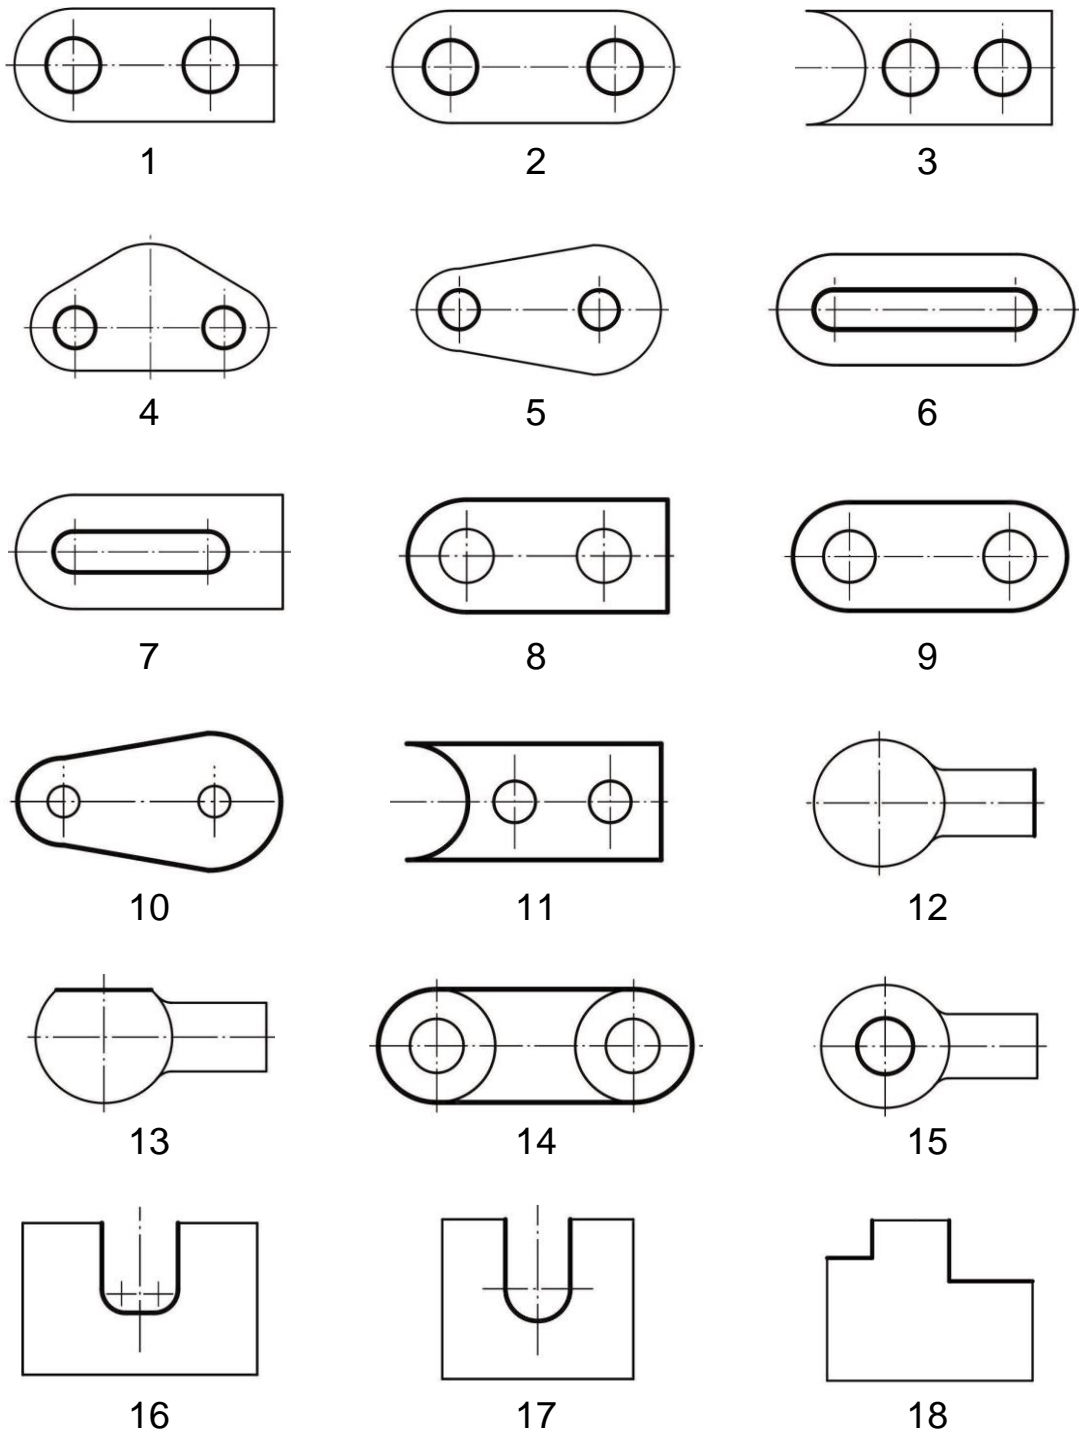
Варіанти оброблюваних поверхонь: товста лінія – поверхня, що оброблюється, тонка – контури деталі
